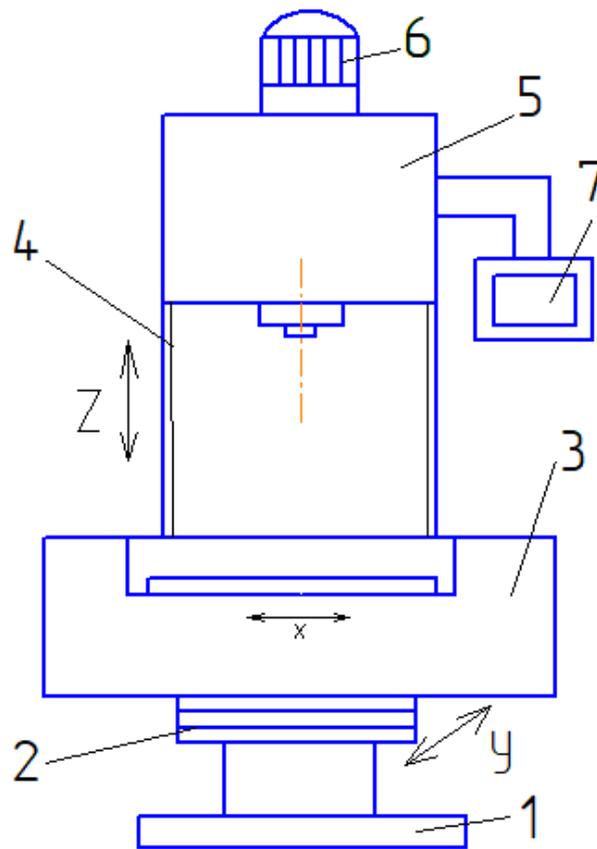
Компоновка вертикально-сверлильного станка с ЧПУ
